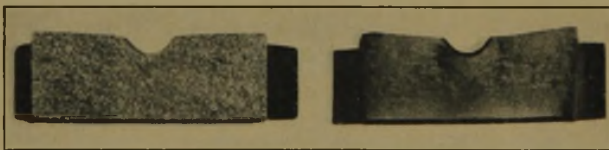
Proben mit ungekerbter Nut. Bild 44.
